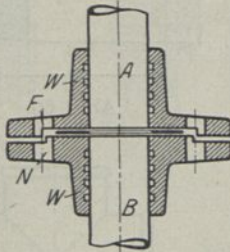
Aufgedrillte Flanschen mit Federn und Nut.
